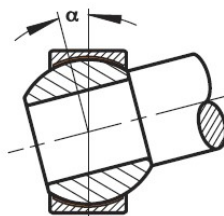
Допустимий кут повороту сферичного підшипника
